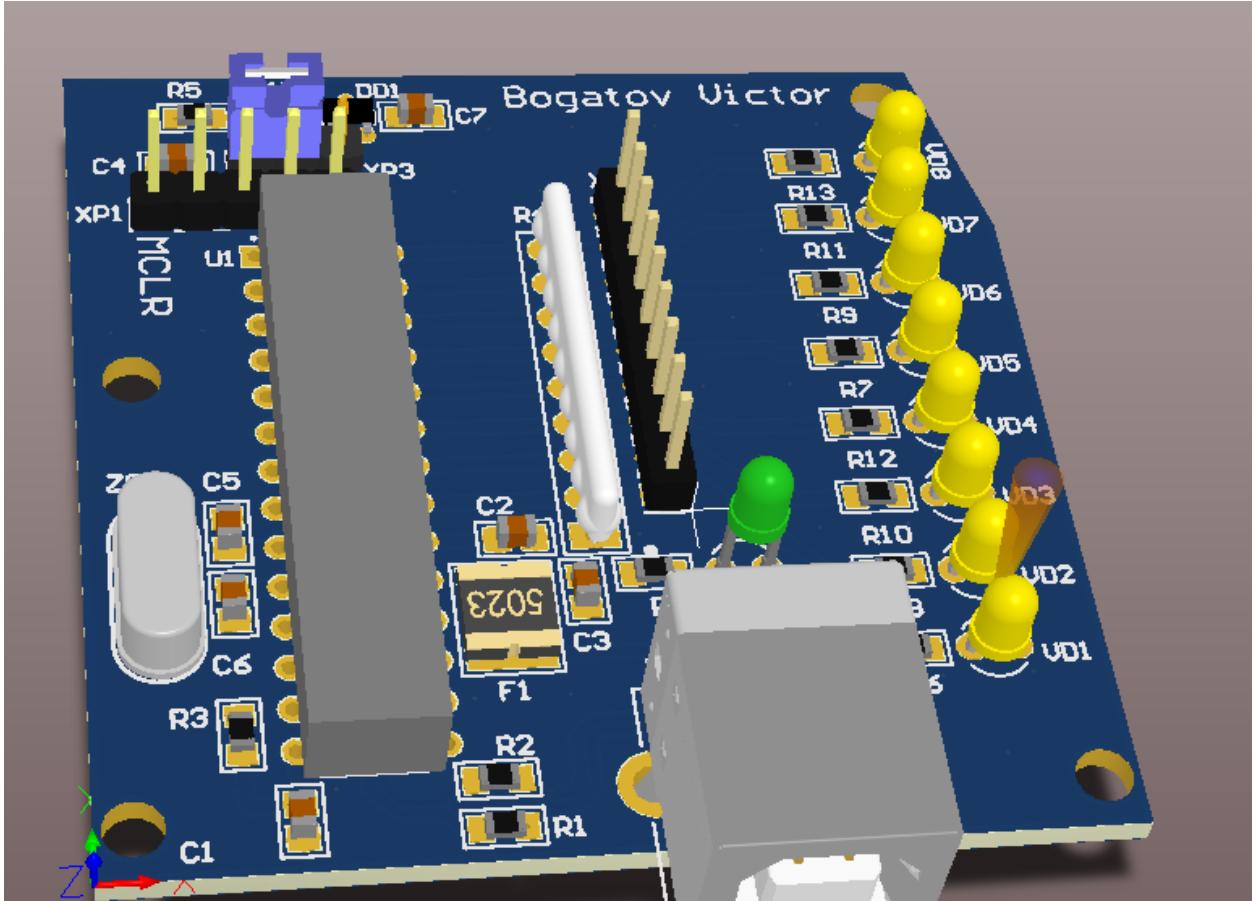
3D модель печатной платы в PCB-редакторе вид сверху
